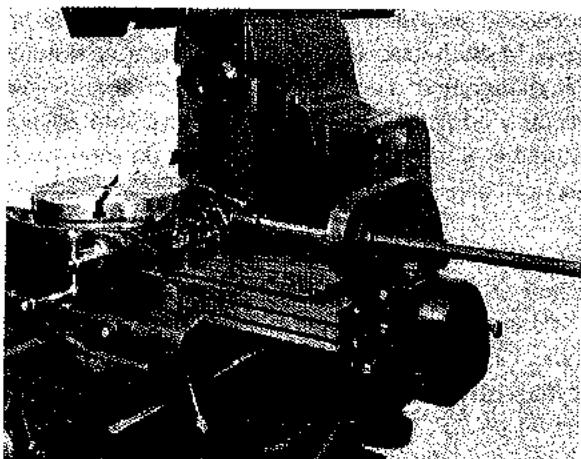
Plato giratorio y dispositivo de accionamiento del mismo (Cincinnati Milling Machine Co.)
